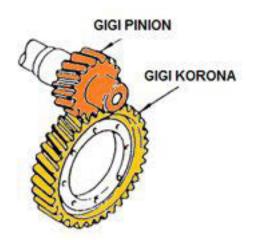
Penggerak roda gigi hypoid (hypoid Bevel Gear)
